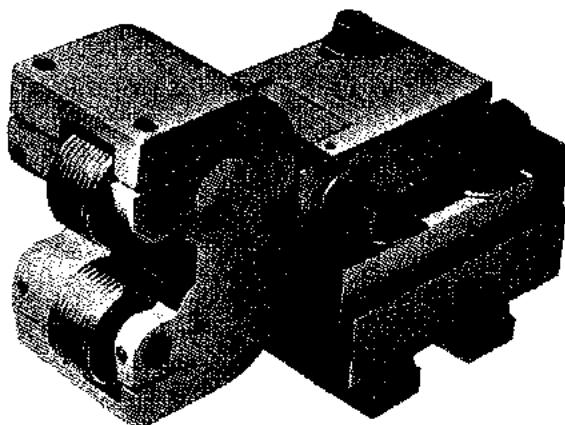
Accesorio de laminación de roscas (Reed Rolled Thread Die Co.)
